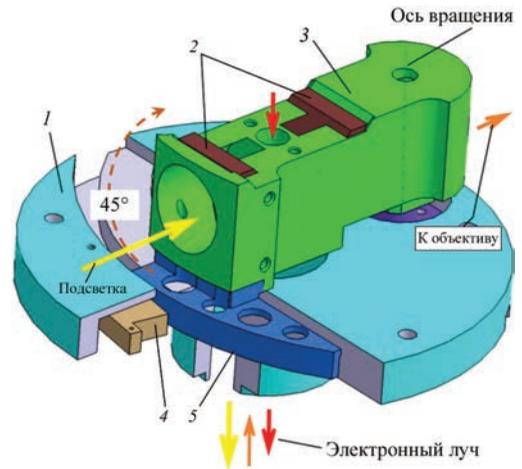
Общий вид подвижного блока зеркал: 1 — корпус видеомодуля; 2 — зеркала; 3 — поворотный корпус зеркал; 4 — пьезокартридж; 5 — поверхность пьезопривода
